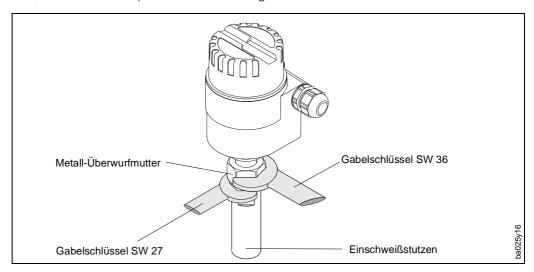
Montage des Einschweißstutzens für Stahlrohrleitungen
